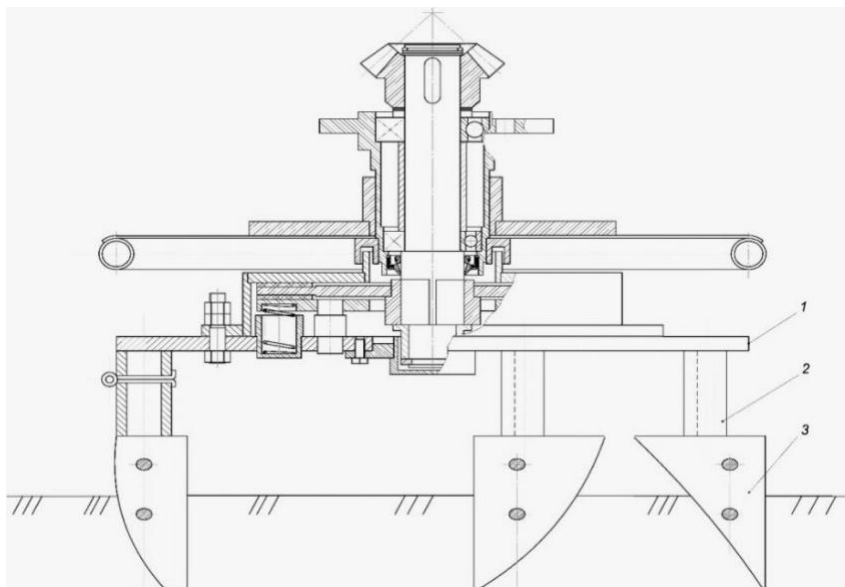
Конструктивно-технологічна схема фрезерної машини з позначенням основних вузлів: 1 – рама; 2 – опорне колесо; 3 – привідний вал; 4 – ротори; 5 – диск; 6 – стійка; 7 – ніж.
